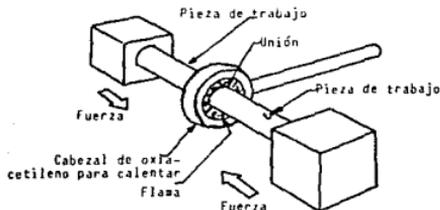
Arreglo para calentar piezas en soldadura a presión con oxiacetileno con el método de claro estrecho.
